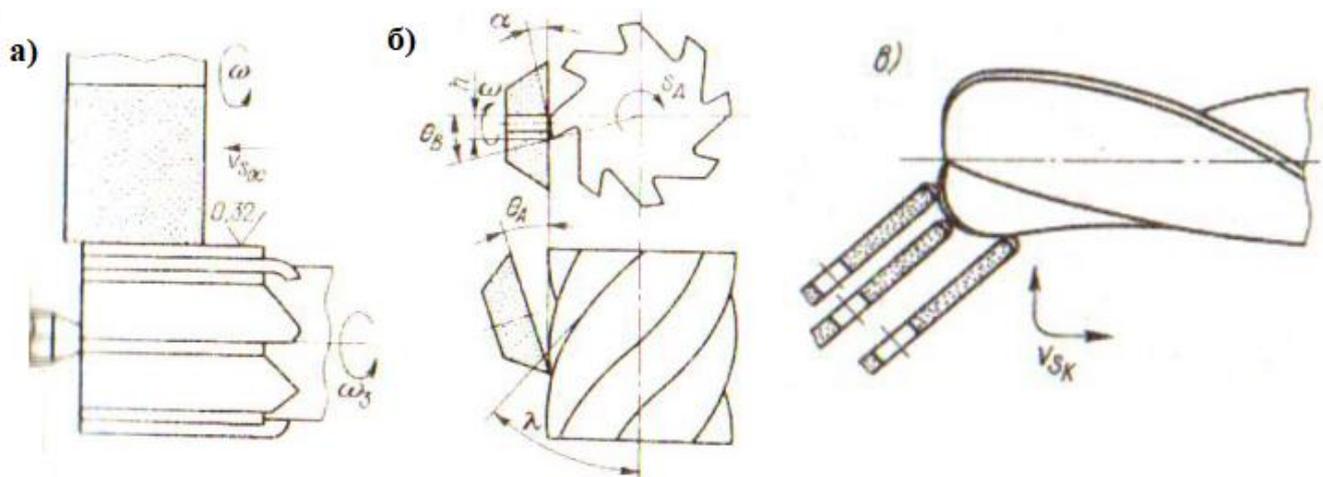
Схема заточки передней поверхности поверхности резца-а; прорезки стружколомающей канавки-б
